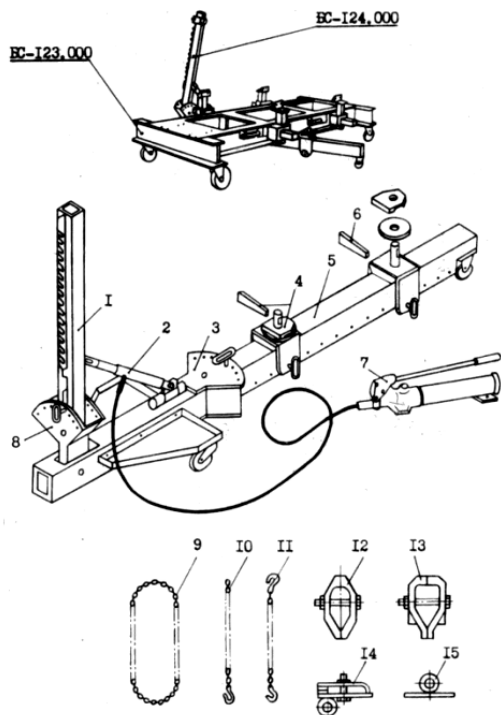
Общий вид устройства для правки кузовов BC-124.000
